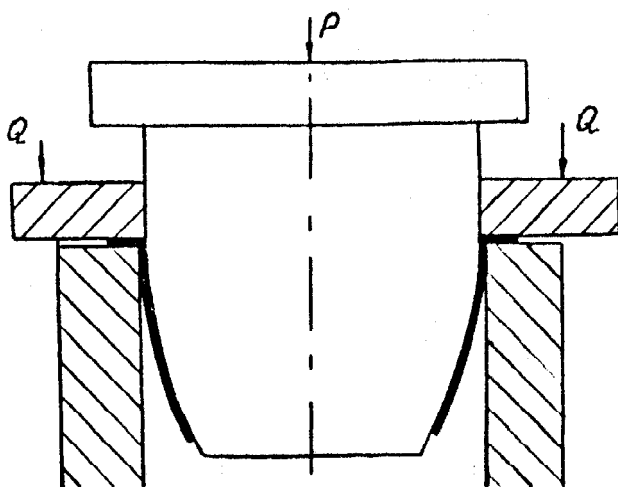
Штамповка в инструментальном штампе тонкостенных заготовок
